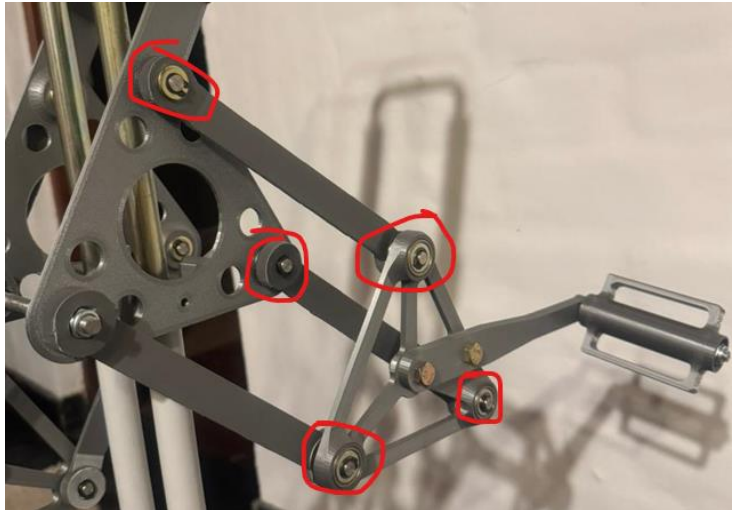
Vista de la planchuela modificada mejorando el calce del rodamiento
